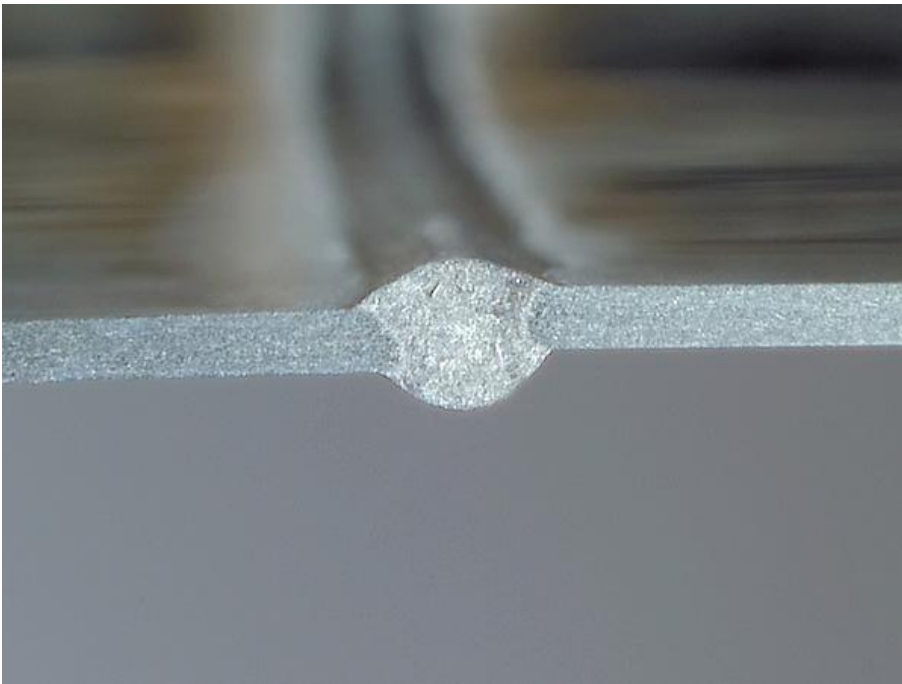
Стыковой шов между двумя листами AlMg3 толщиной всего лишь 0,8 мм: сваренные с использованием технологии СМТ без использования каких-либо зажимов, фиксаторов или опорных устройств для сварочной ванны.
